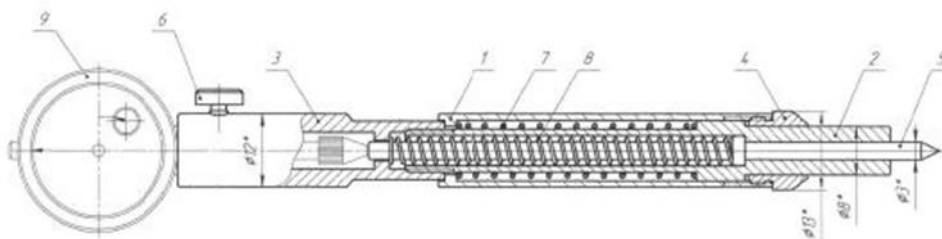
Схематичне зображення пристрою для визначення твердості кісткової тканини: 1- зовнішній корпус; 2- корпус щупа; 3- наконечник; 4- внутрішній корпус; 5- конусний наконечник; 6- фіксований гвинт; 7- виїмка; 8- пружина; 9- вимірювальний індикатор
